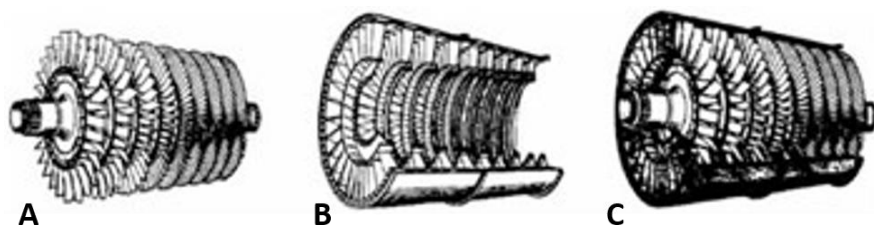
Compressor Axial. A) Rotor com palhetas; B) Estator com palhetas; C) Compressor montado (Courtesy of Pratt & Whitney) [17].
